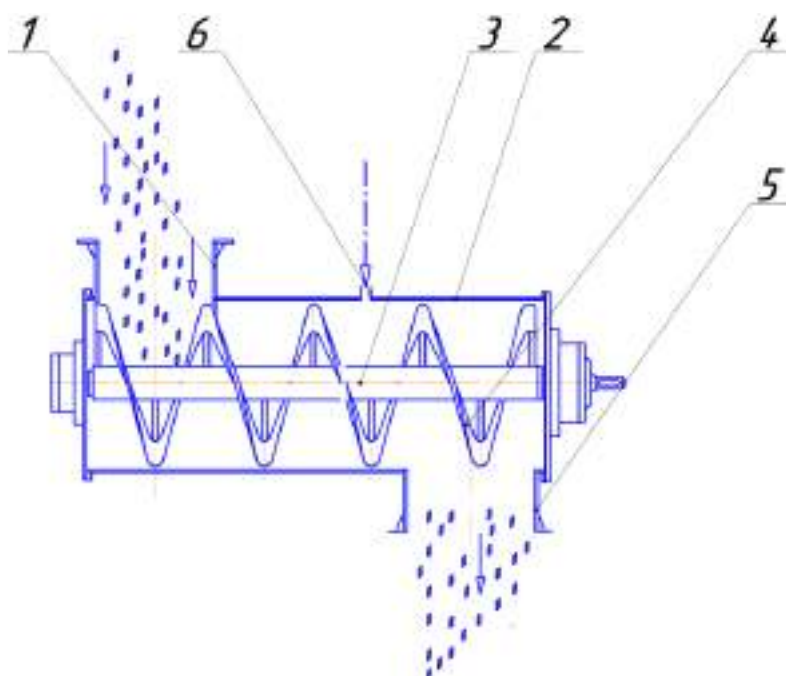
Схема змішувача: 1 – Завантажувальна горловина; 2 – циліндричний корпус; 3 – вал; 4 – шнекова стрічка; 5 – розвантажувальна горловина; 6 – форсунка.
